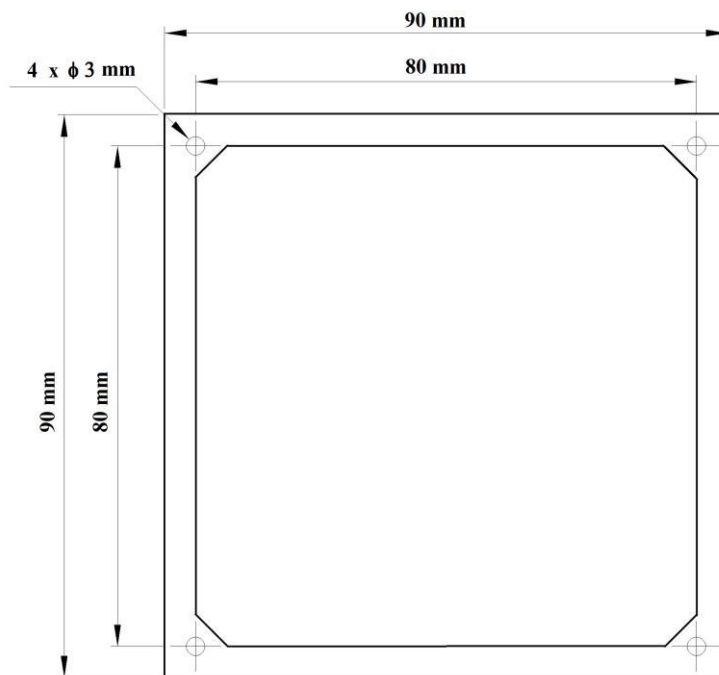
带有四个 $\phi 3$ mm 安装孔 PCB 尺寸
